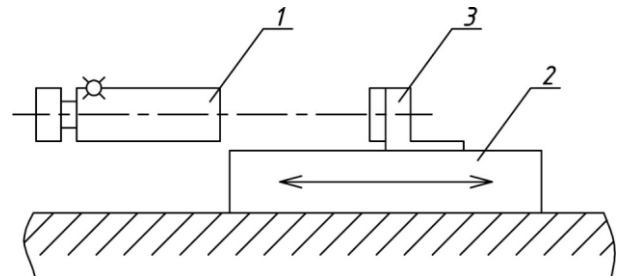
Схема контролю сталості кутового позиціонування робочих вузлів верстата: 1 – автоколіматори; 2 – контрольований робочий вузол; 3 – плоске дзеркало
